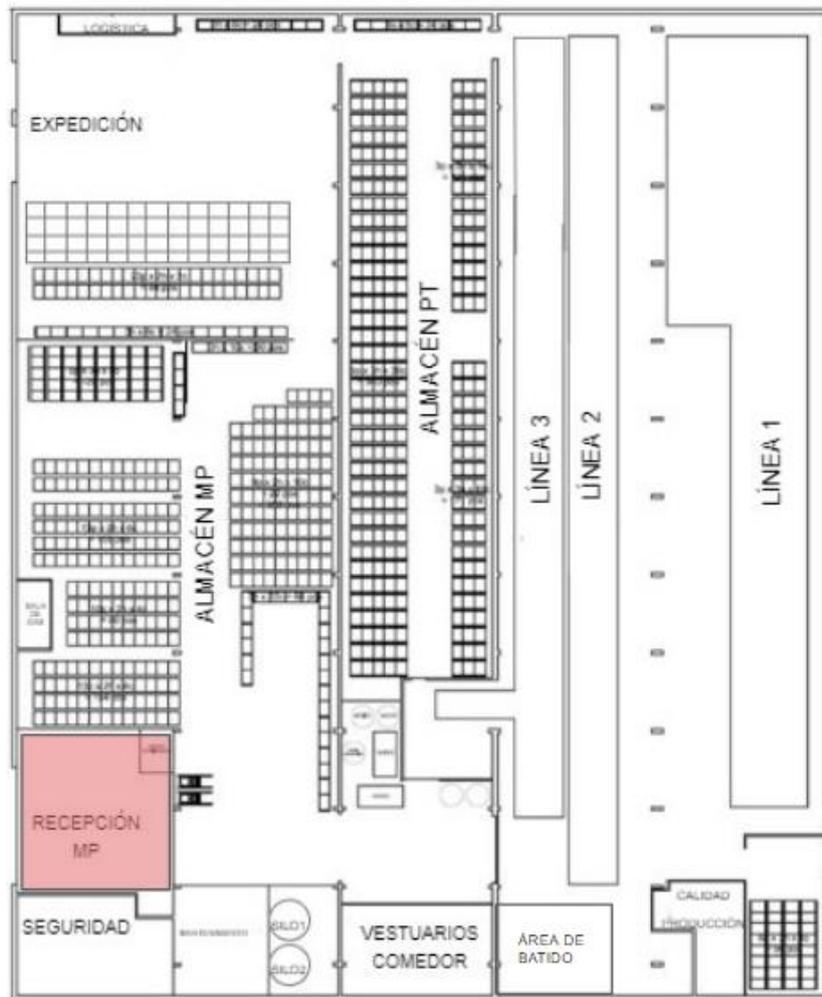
Layout de la planta con área de recepción de MP sombreada en rojo
